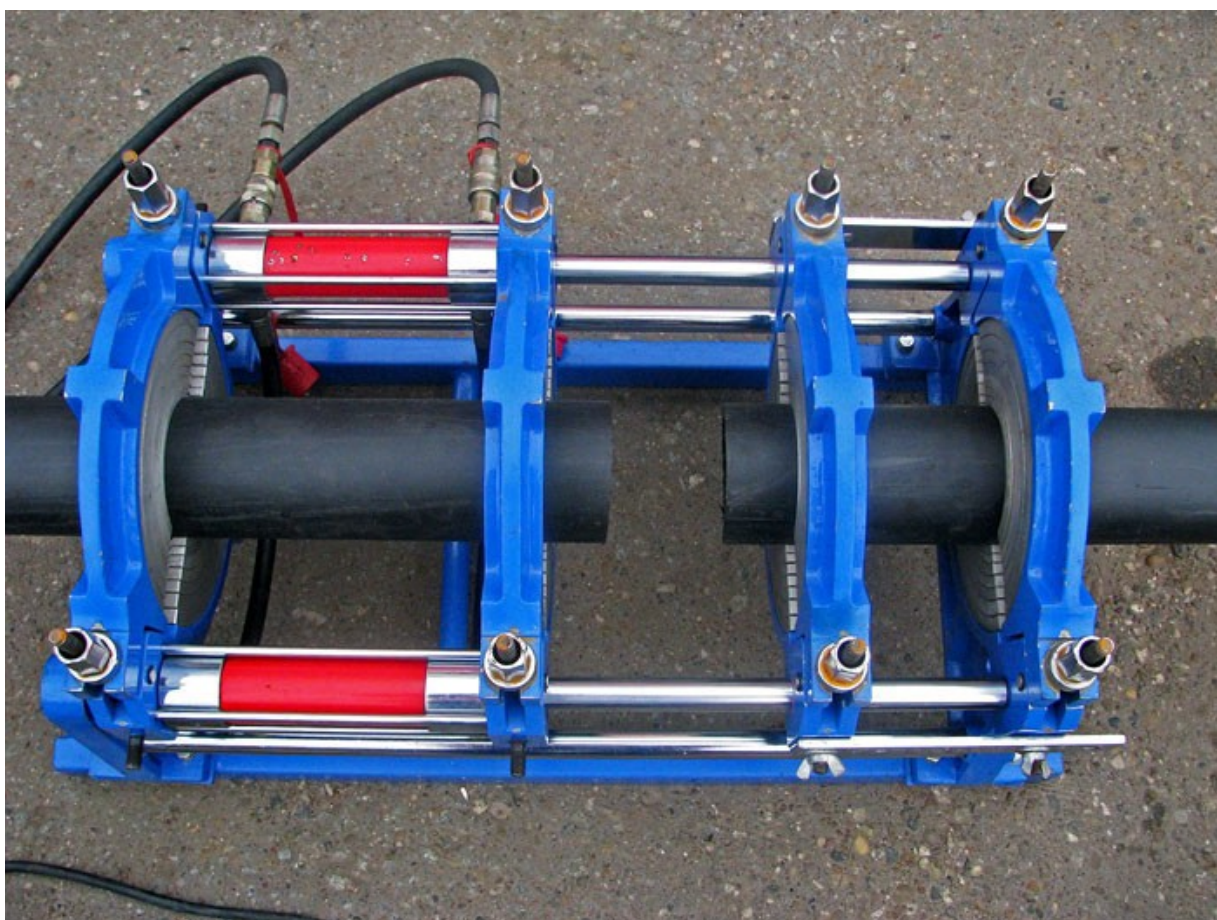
Общий вид устройства для сварки труб из сшитого полиэтилена
